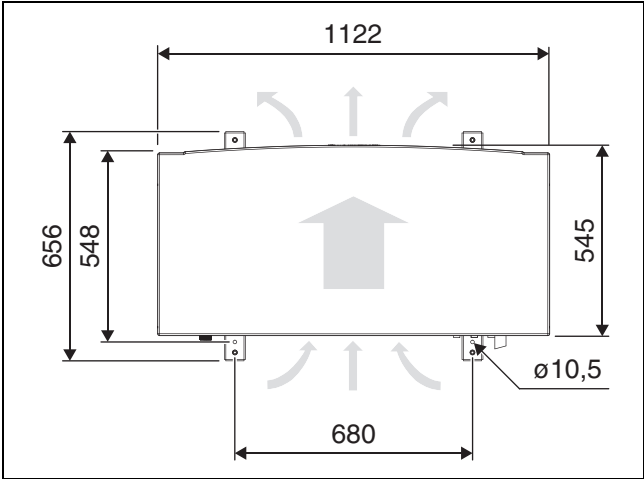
Dimensjoner til varmepumpetype 413-417, sett ovenfra
